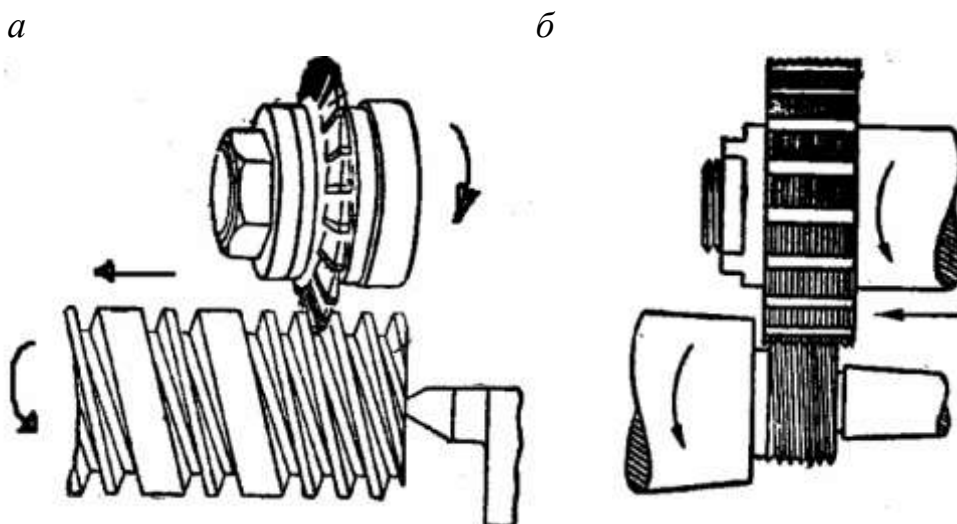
Обработка резьбы на резьбофрезерных станках:
